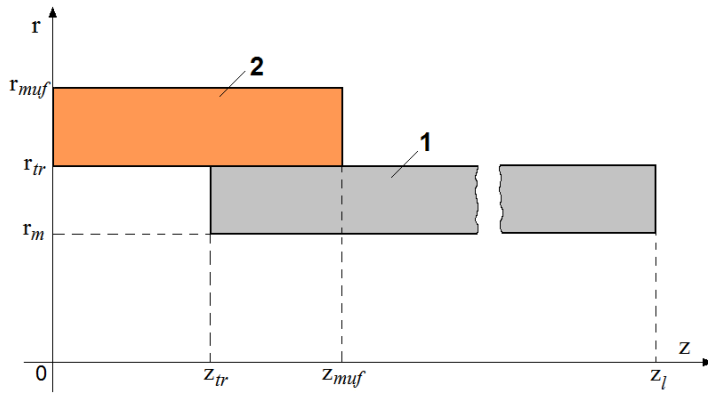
Расчетная схема раструбной сварки полиэтиленовых труб:
